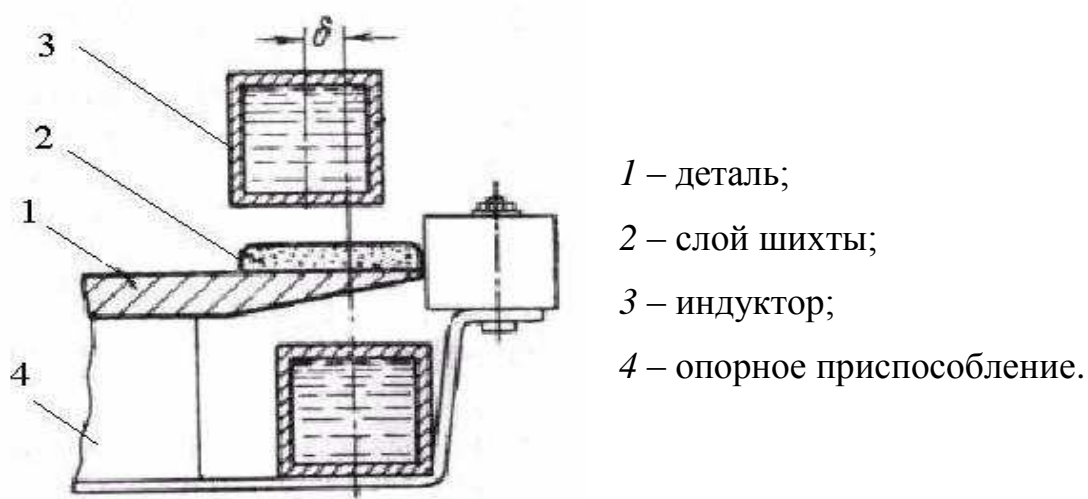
Схема расположения наплавляемой детали в индукторе:
